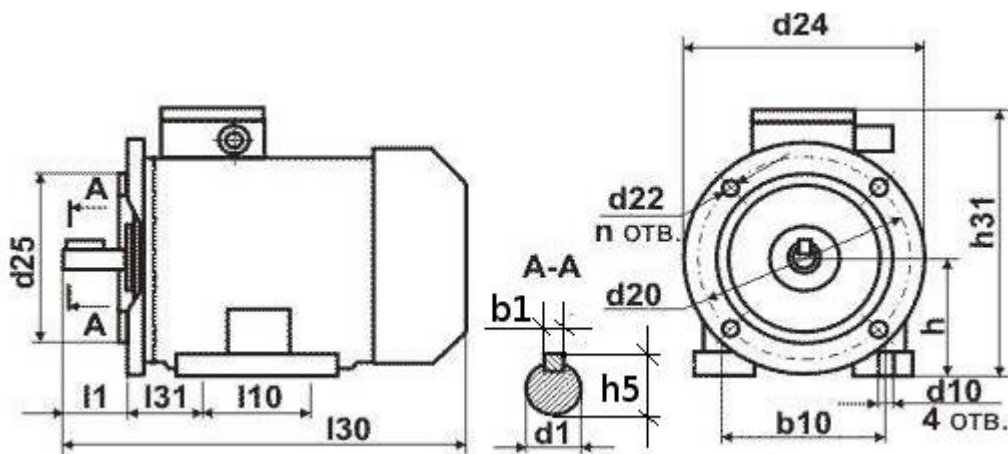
Габаритные и присоединительные размеры двигателя
